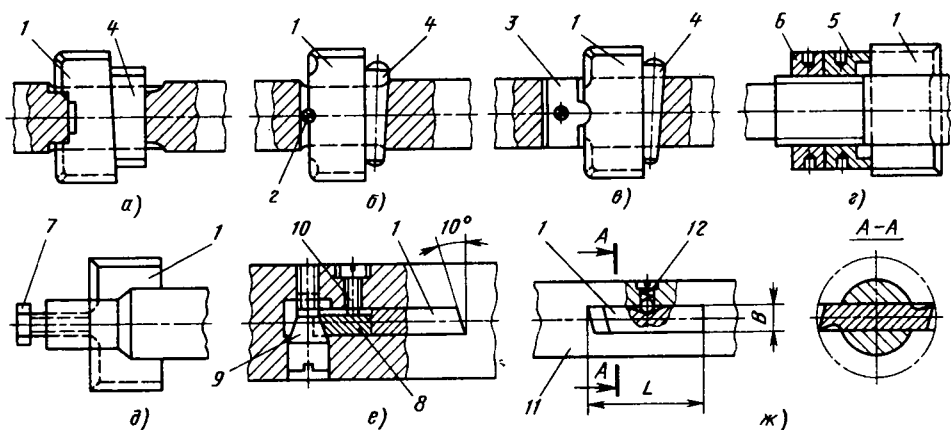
Основные типы крепления двусторонних пластинчатых резцов и блоков в оправках
